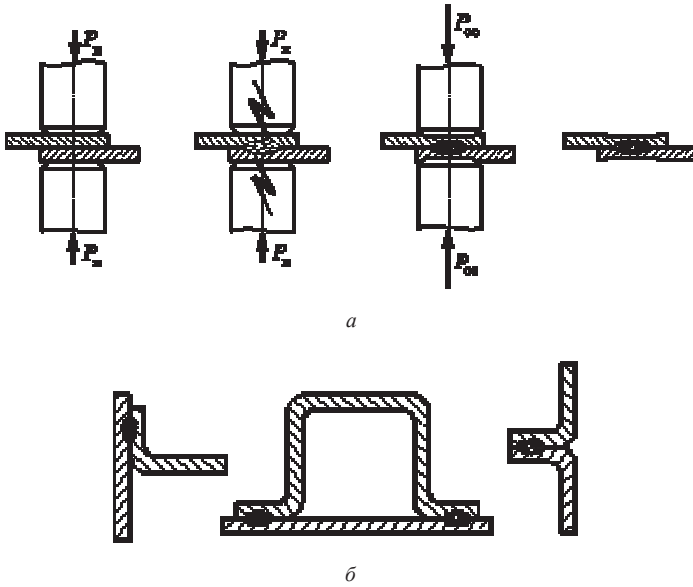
Точечная контактная сварка: *а* – схема и стадии сварки; *б* – типы сварных соединений
